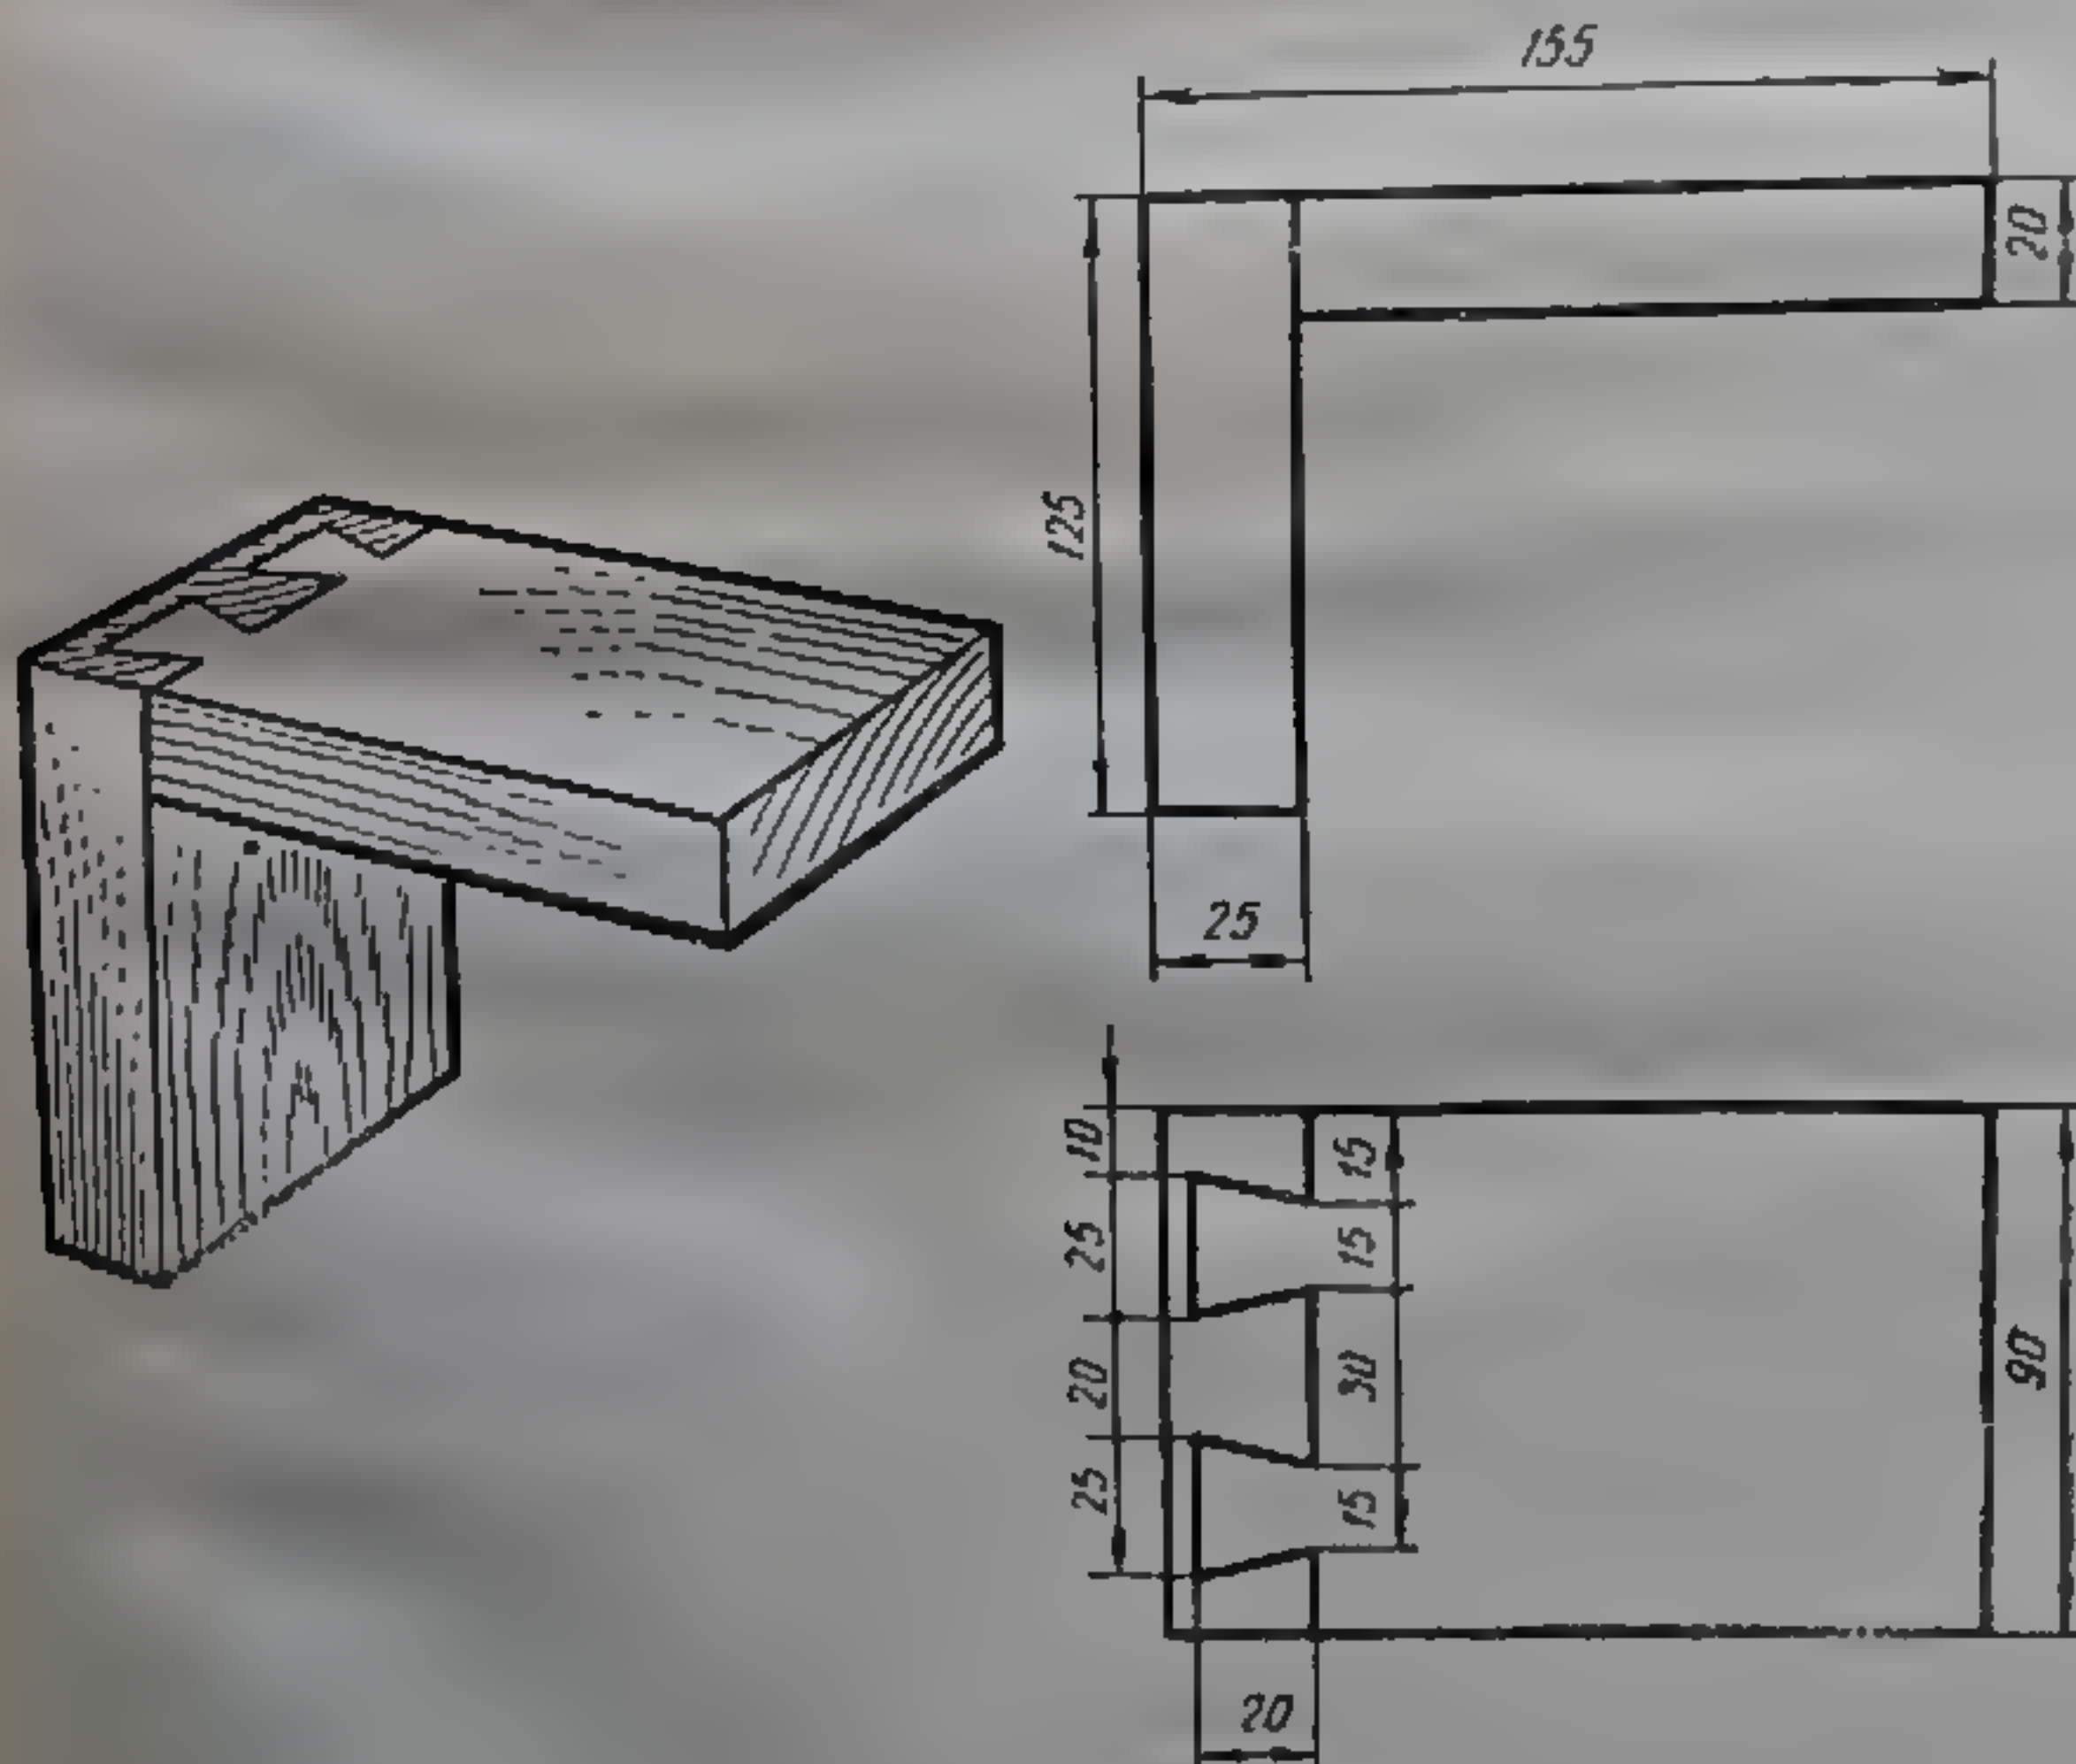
Чертежи ящичного соединения на шип «ласточкин хвост» вполупотай.
